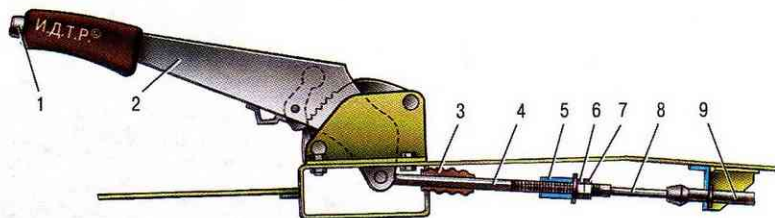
Привод стояночного тормозной системы: 1 - кнопка фиксации рычага; 2 - рычаг привода стояночного тормоза; 3 - защитный чехол; 4 - тяга; 5 - уравниватель троса; 6 - регулировочная гайка; 7 - контргайка; 8 - трос; 9 - оболочка троса
